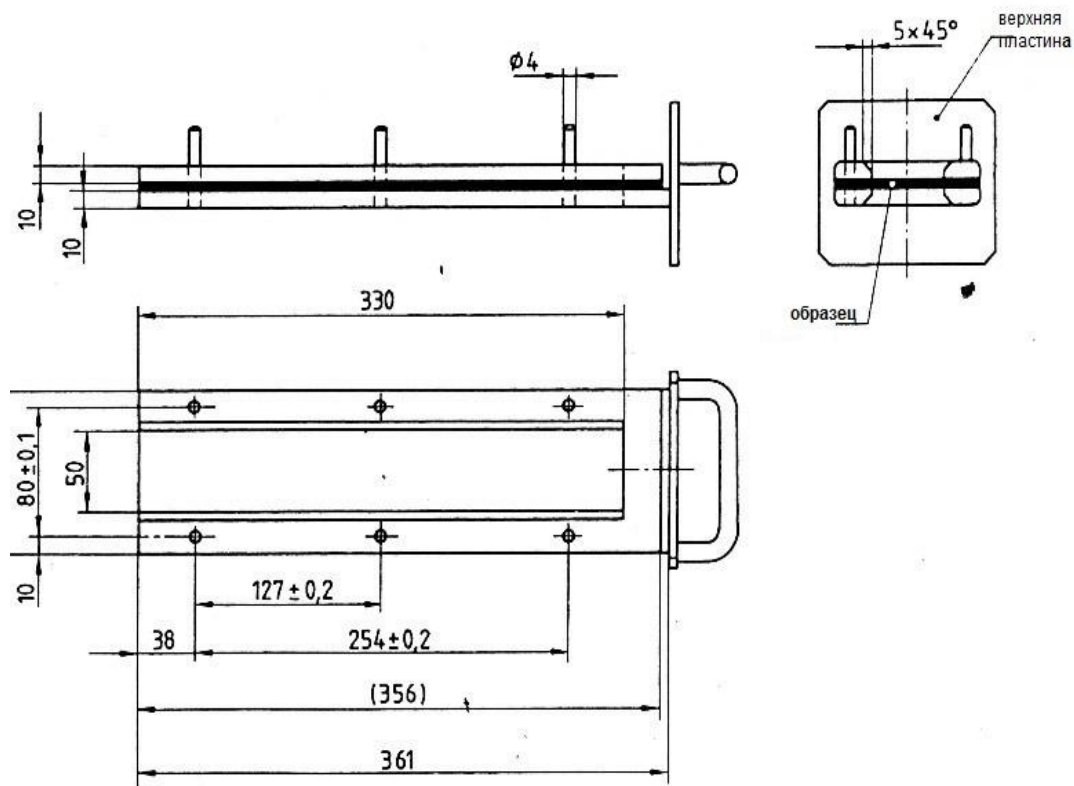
Держатель образца материала (размеры в миллиметрах)
